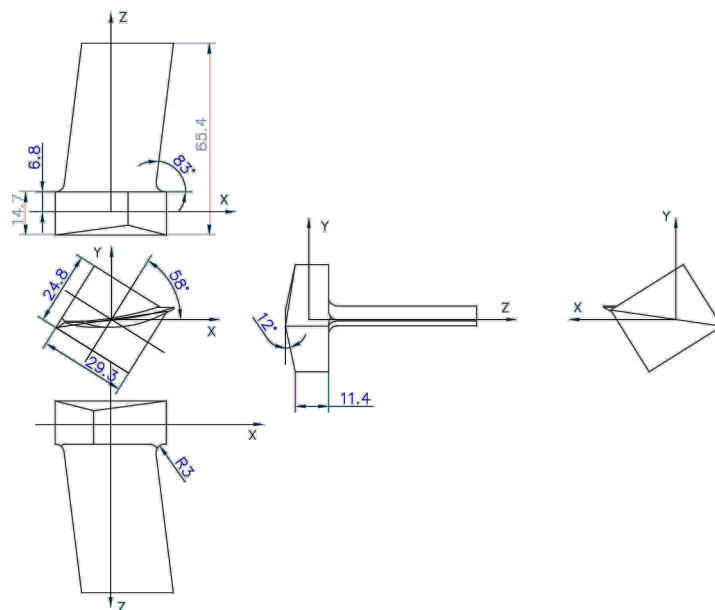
Чертеж лопатки авиационного двигателя из жаропрочного деформируемого сплава на основе никеля
